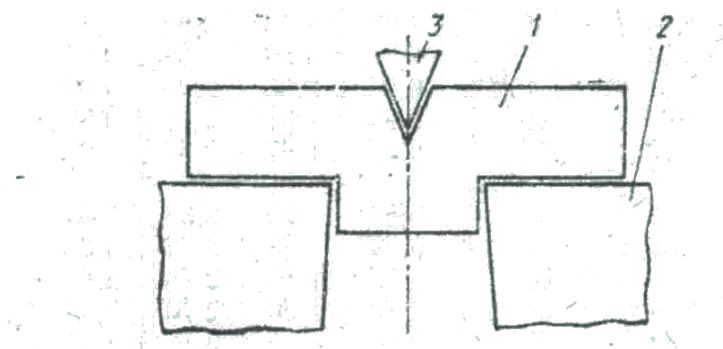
Шаблон для установки опор симметрично относительно ножа маятника [3]
